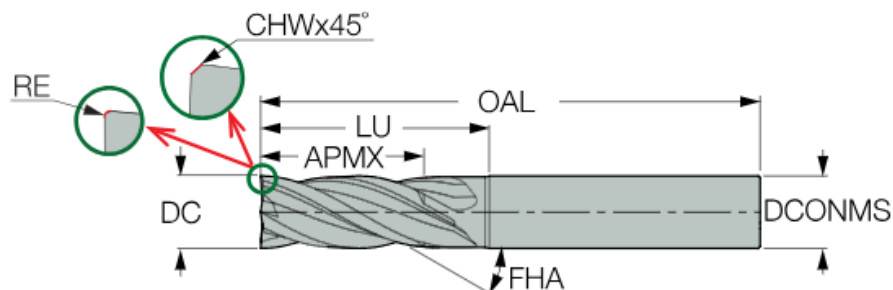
Фреза кінцева EC-E4L 08-18/26C08CFR0.3
